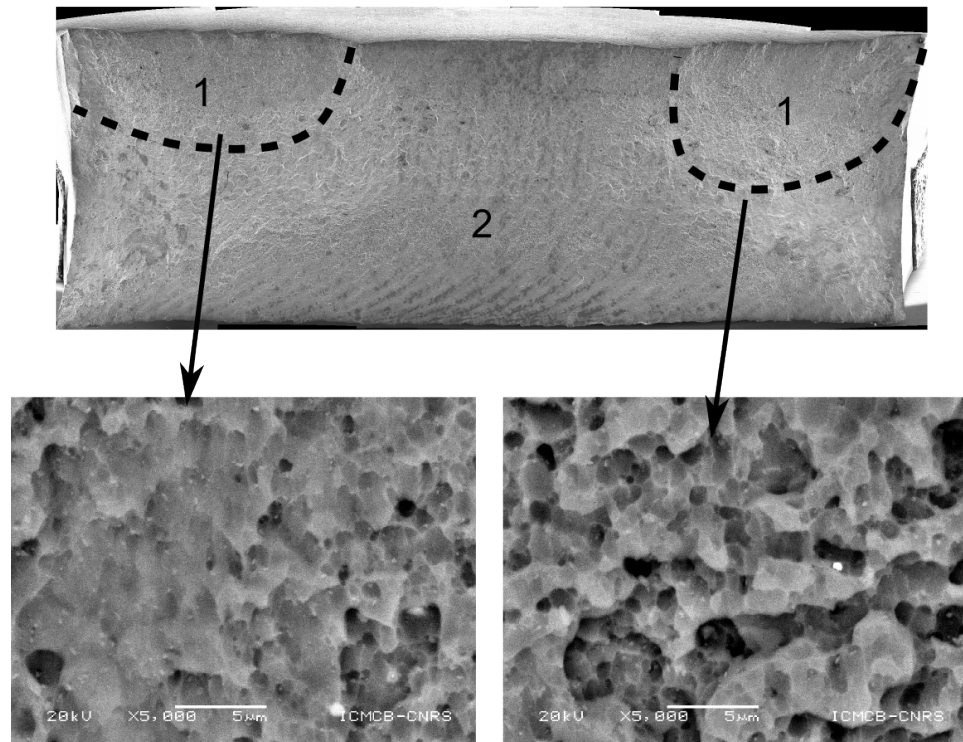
Rupture des joints soudés par FSW en alliage d'aluminium 7449-T79/ 2050-T851 sous chargement de traction monotone quasi-statique
